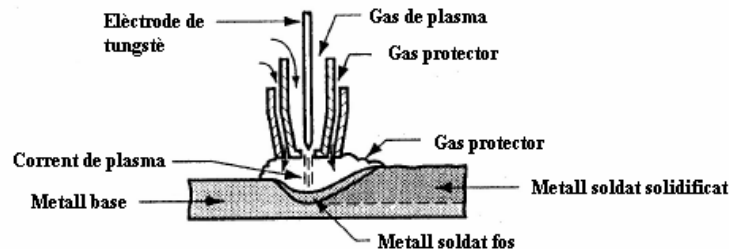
El Gas “El escut protector”. El escut de gas que expulsa la torxa és molt important per assegurar soldadures de qualitat.
